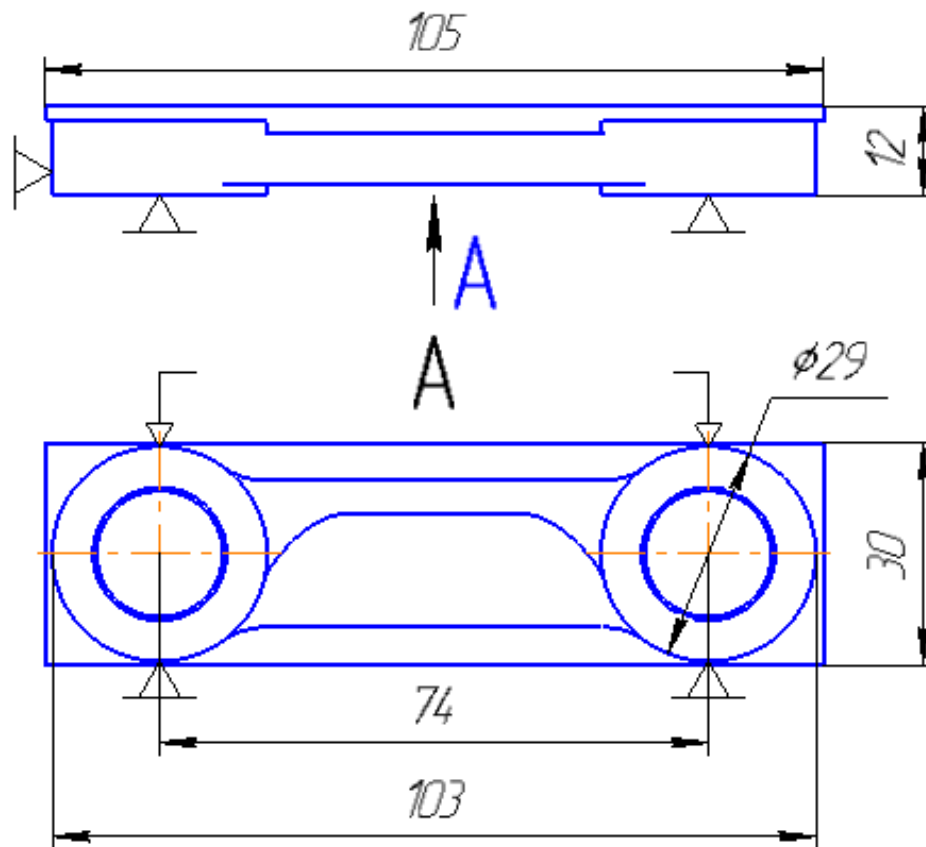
Схема базування та кріплення деталі на операції 005 Фрезерна з ЧПК
